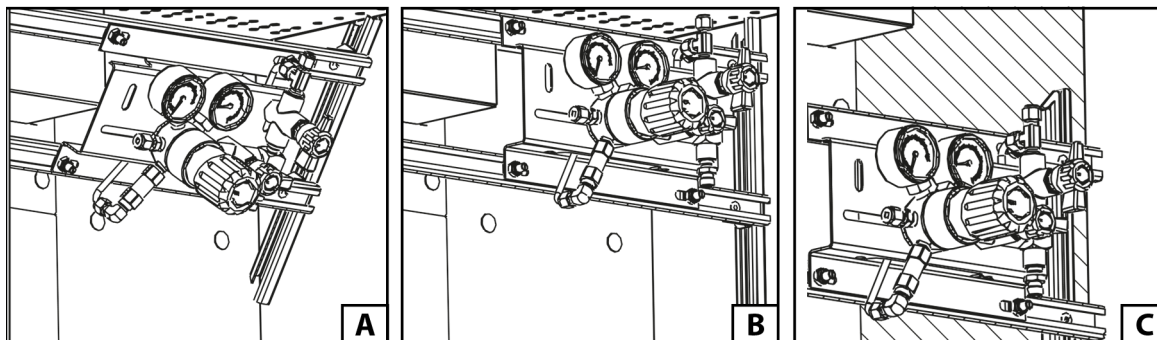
Cambio del soporte para valvulería (SUPREME standard)
